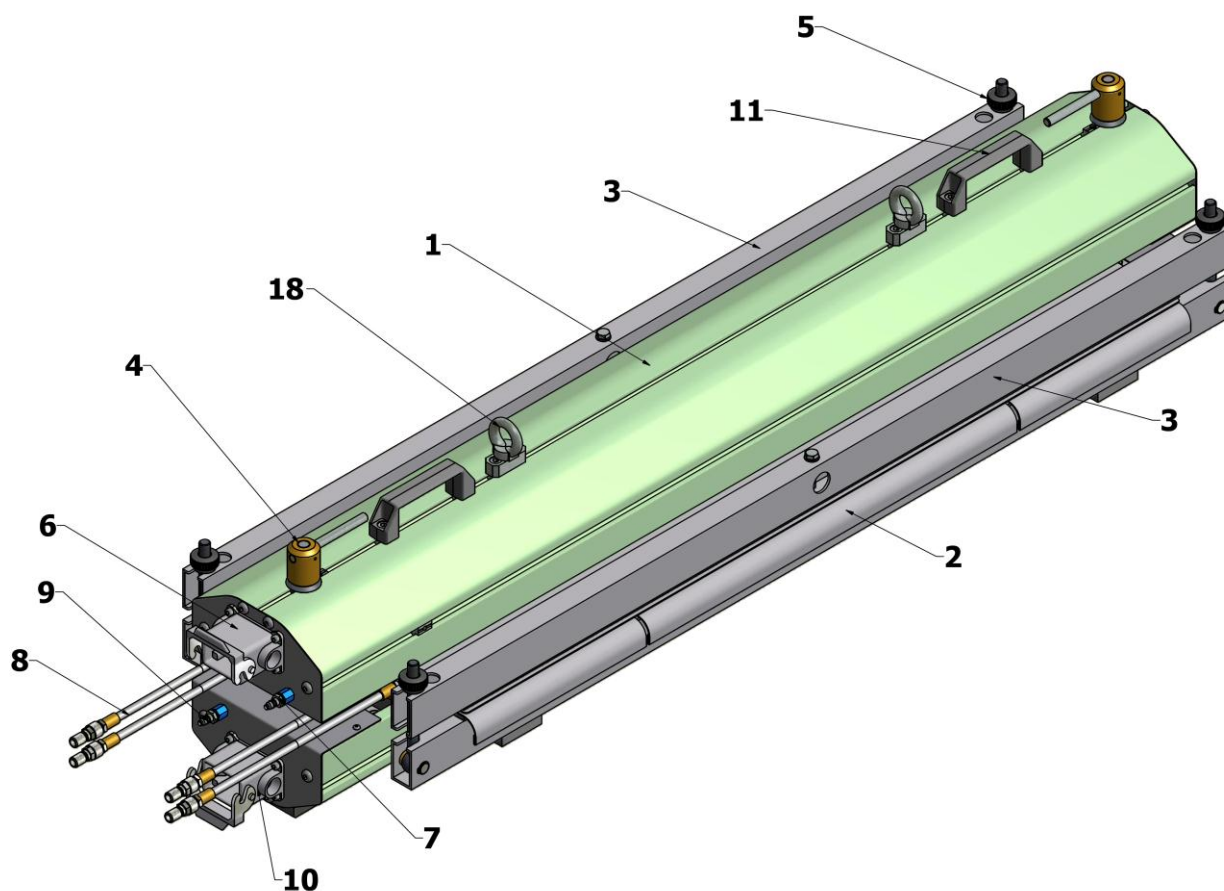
Vue d'ensemble de la presse modèle PM-09/160W
